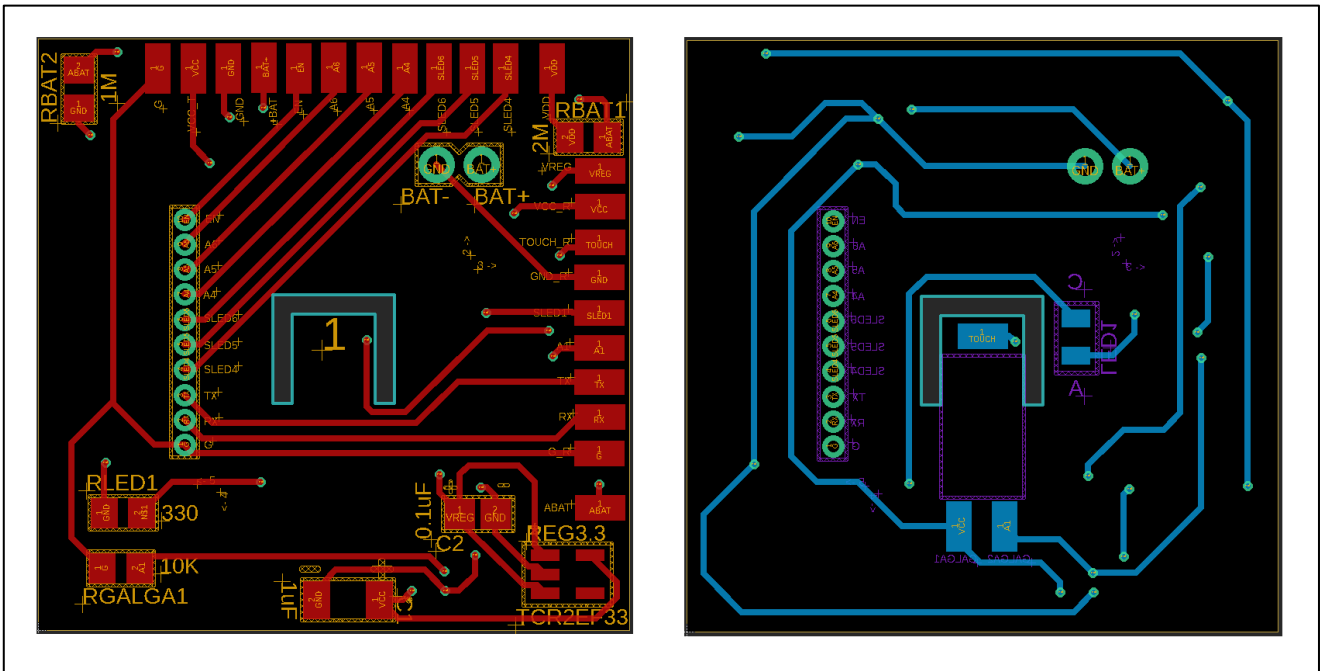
PCB de la Cara 1. Capa TOP y BOTTOM.
